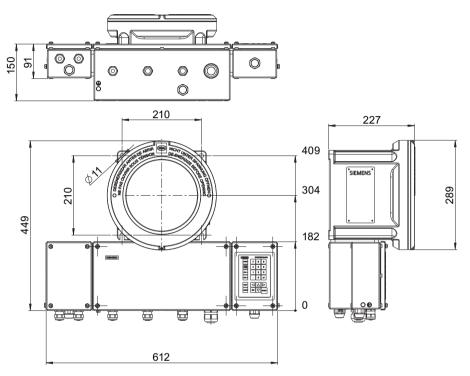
Disegno quotato, tutte le dimensioni in mm
